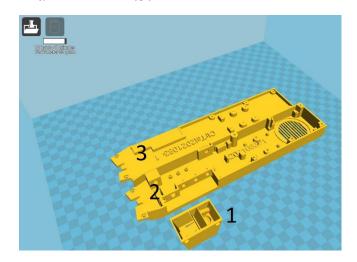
Детали корпуса в программе Cura. 1 — корпус светодиода — фотодиода; 2 — нижняя часть корпуса; 3- верхняя часть корпуса.
